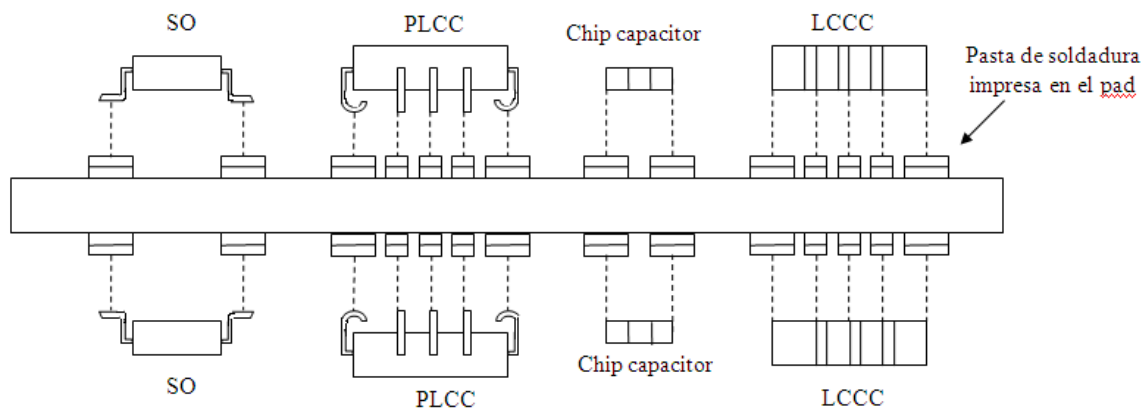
Esquemático de la placa de montaje superficial tipo I [2].
